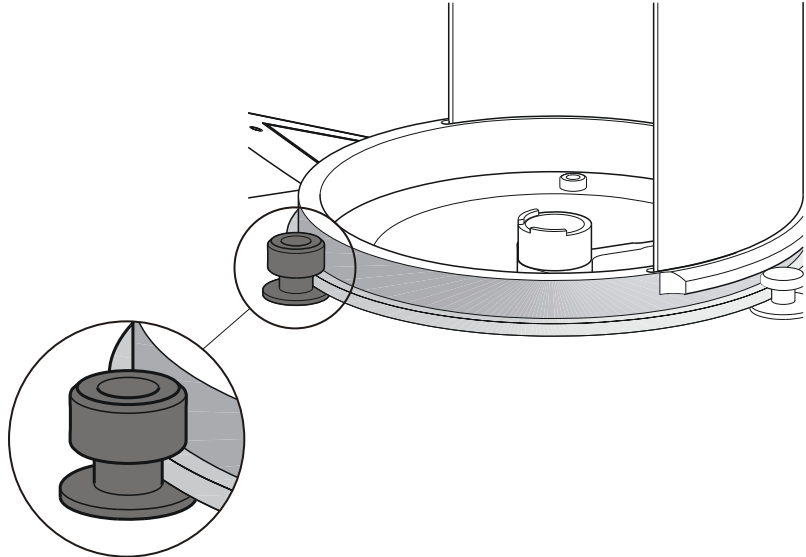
Anschlag über Gewindeöffnung positionieren
